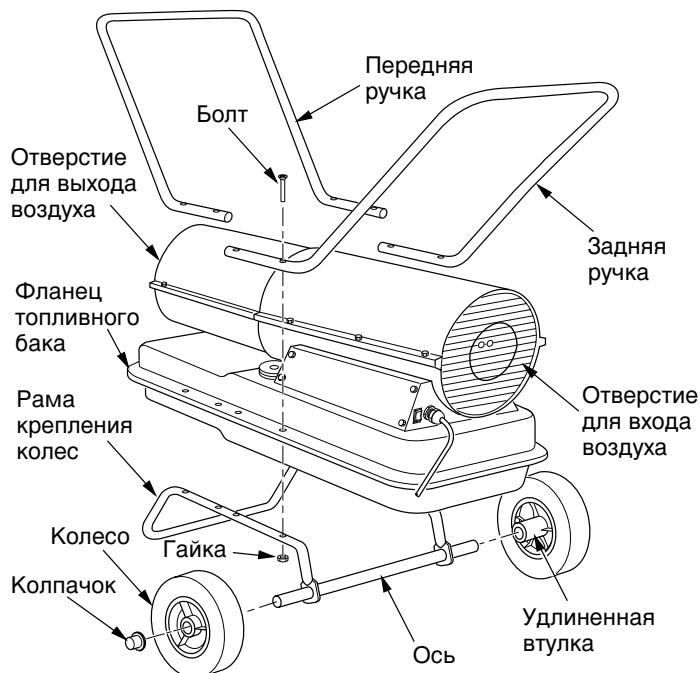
Сборка колес и ручек; только для нагревателей мощностью 30 и 43 кВт
